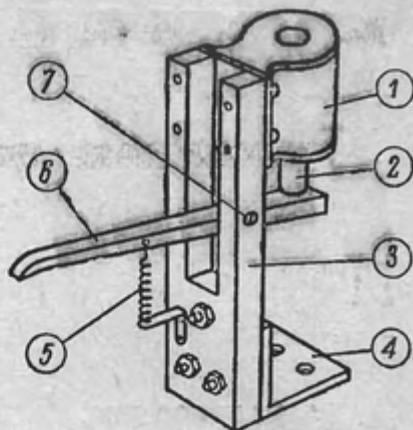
Электромагнитный механизм подошвы ноги: 1 — катушка электромагнита; 2 — сердечник электромагнита; 3 — стойка; 4 — угловой дюралюминий (25×25 мм); 5 — пружина; 6 — собачка; 7 — ось собачки.
